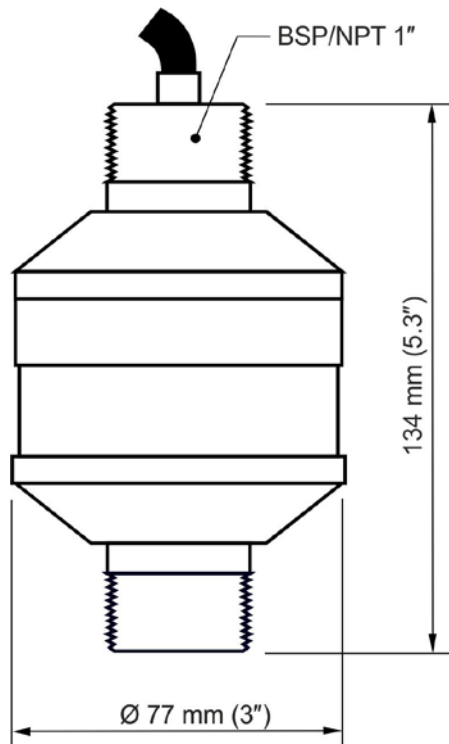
Abmessungen i-Sensor Typ 03 mit Einbaugewinde kableseitig und Frontgewinde
